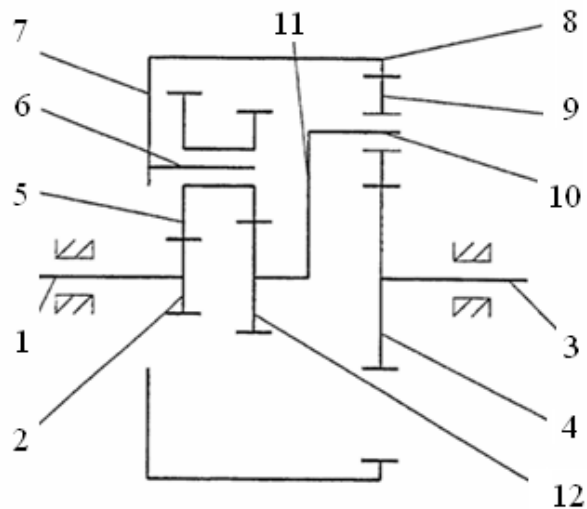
Схема ошибочной конструкции зубчатого вариатора
